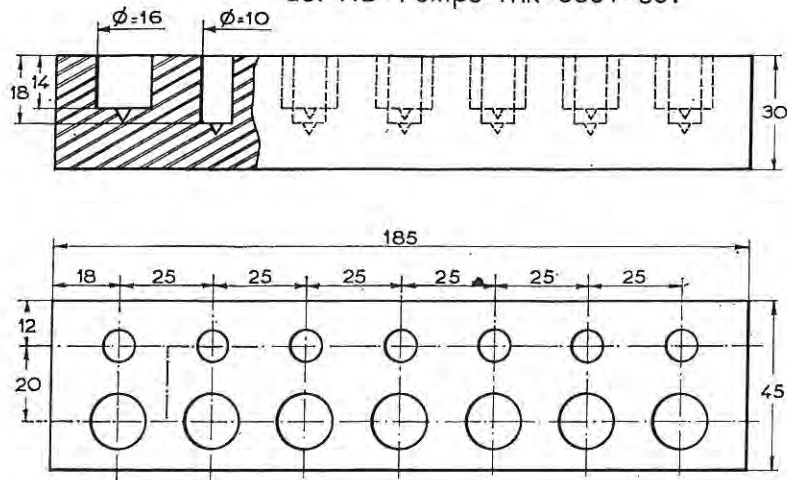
Vorrichtung für Lagerung des Pumpengehäuses - MR-3053-190.
